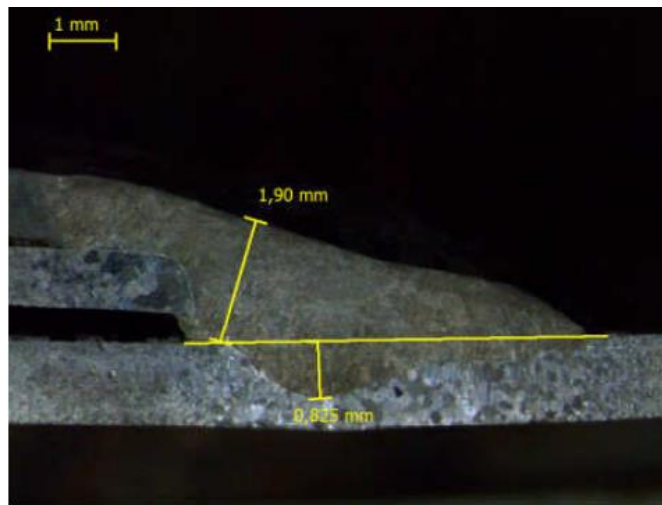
Macrografia do ponto 8 com soldadura circular mais larga (Penetração de 0,825mm)
